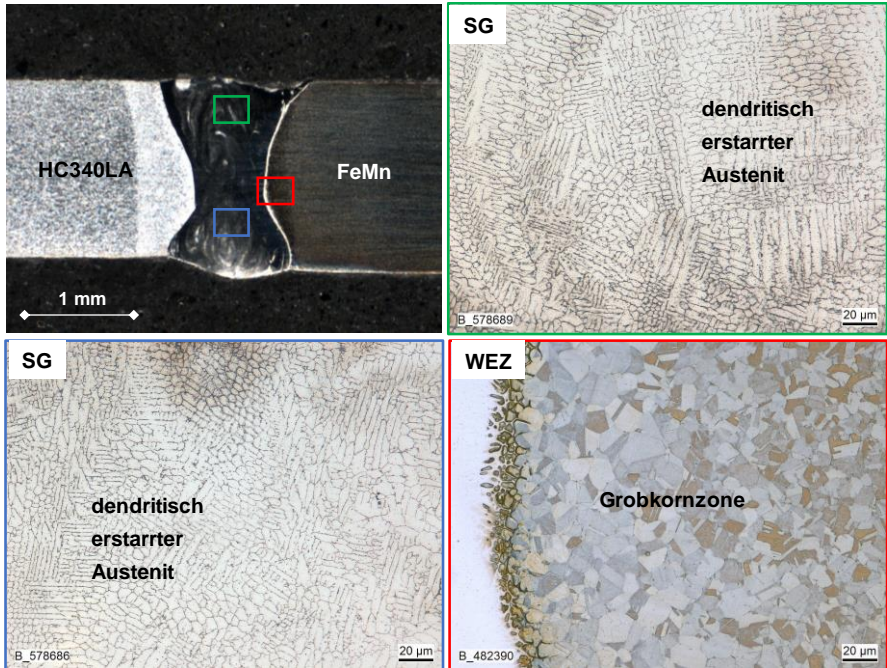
Einfluss des CrNi-Schweißzusatzes auf die Gefügeausbildung
